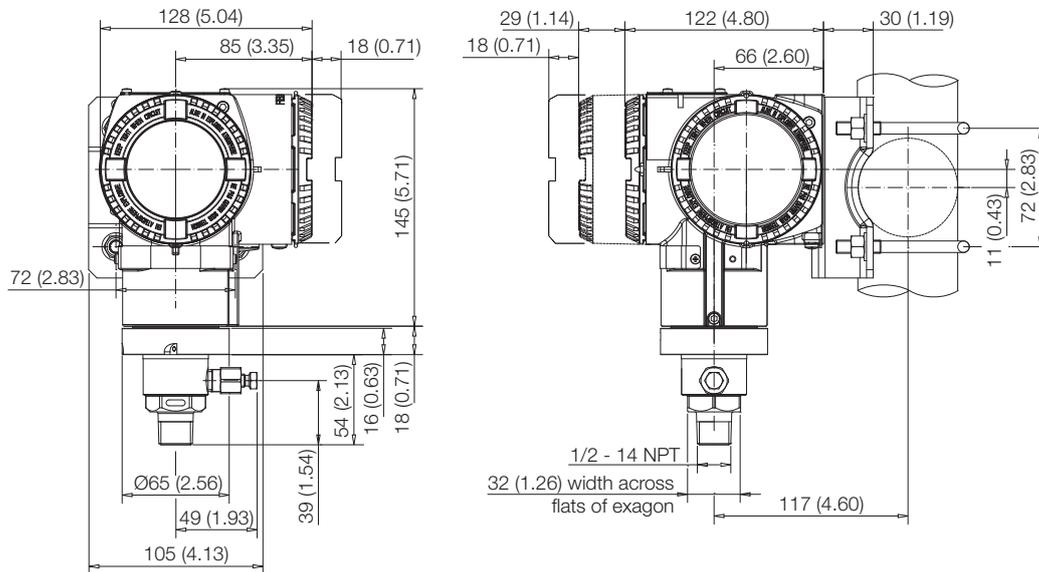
Transmetteur 266H ou 266N équipé d'un boîtier DIN installé sur un tuyau de 2" avec support de montage en option (B2 en acier inoxydable 316L)
